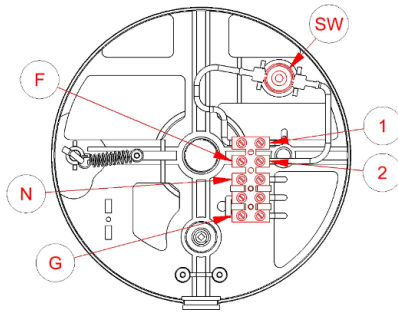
2 KABEL + Thermoschutzschalter
